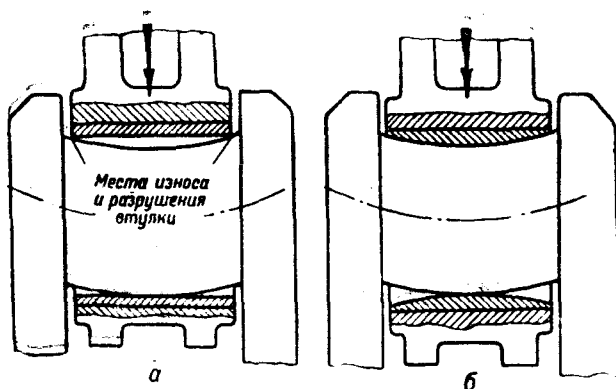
Схема работы втулки кривошипной головки главного шатуна: а—при цилиндрической и б—при гиперболической расточке ее внутренней поверхности
